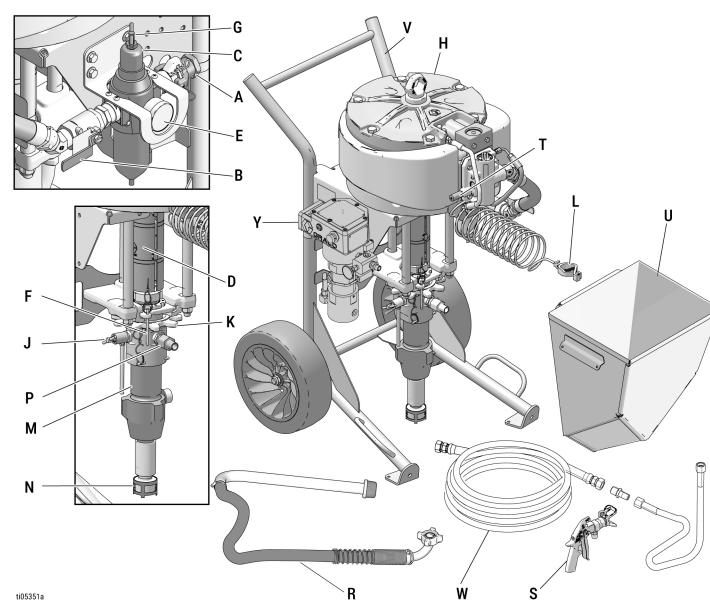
Componentes para o sistema de montagem em carrinho K71PH0
